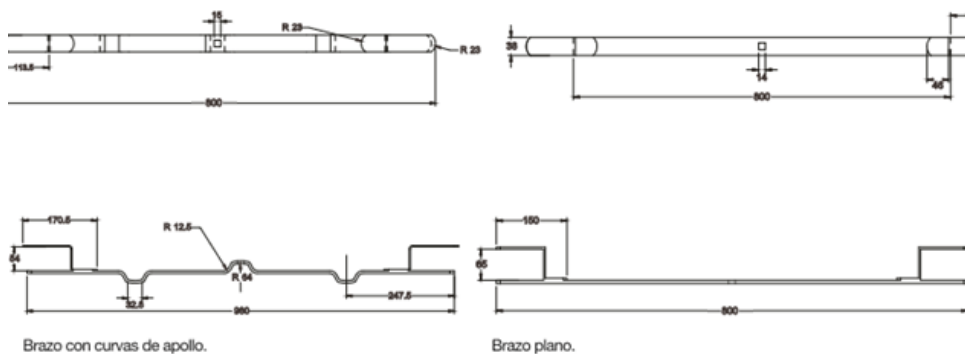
Dimensiones de Cruceta para desarrollo de cable.
